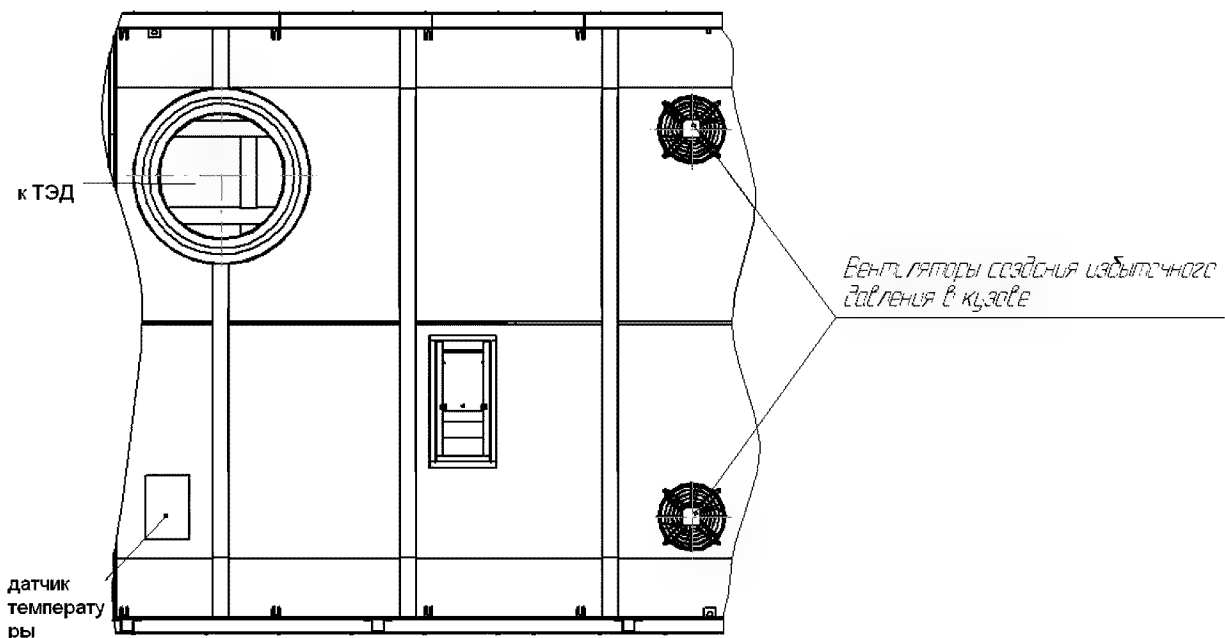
Форкамера вентиляторов избыточного давления вид из машинного отделения.
